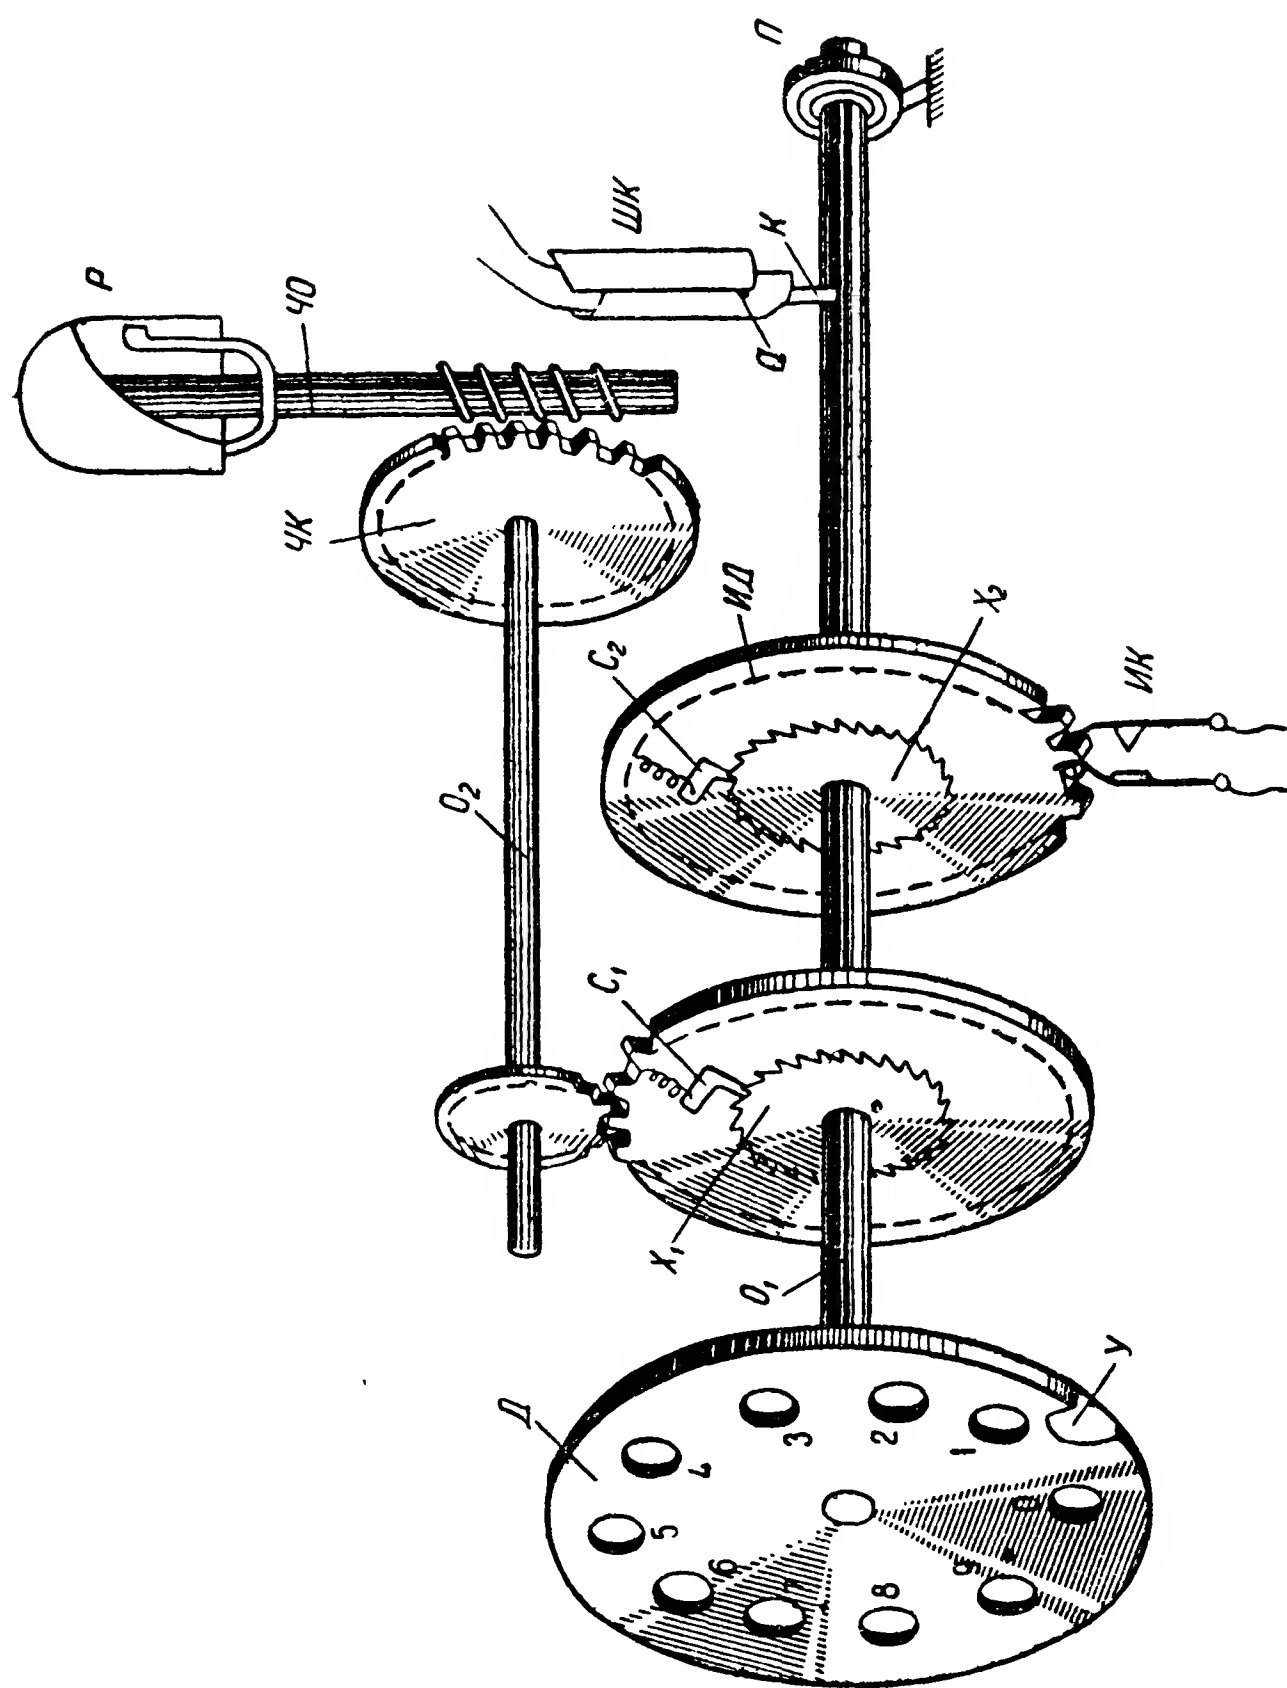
Вариант конструктивной схемы номеронабирателя.
